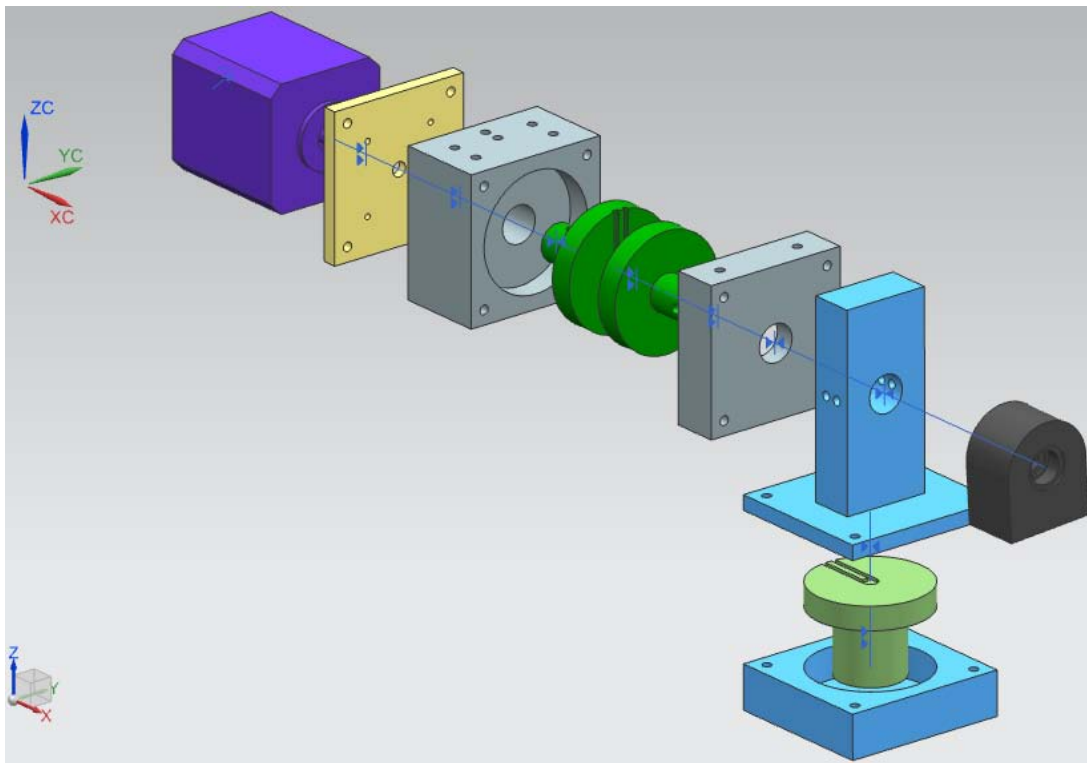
Diseño seleccionado. Ensamble vista explosiva.
